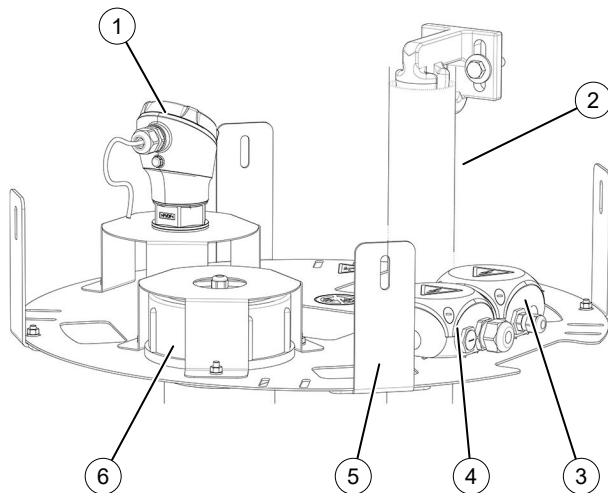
Sensor-Halteplatte Beton-Erdtank
